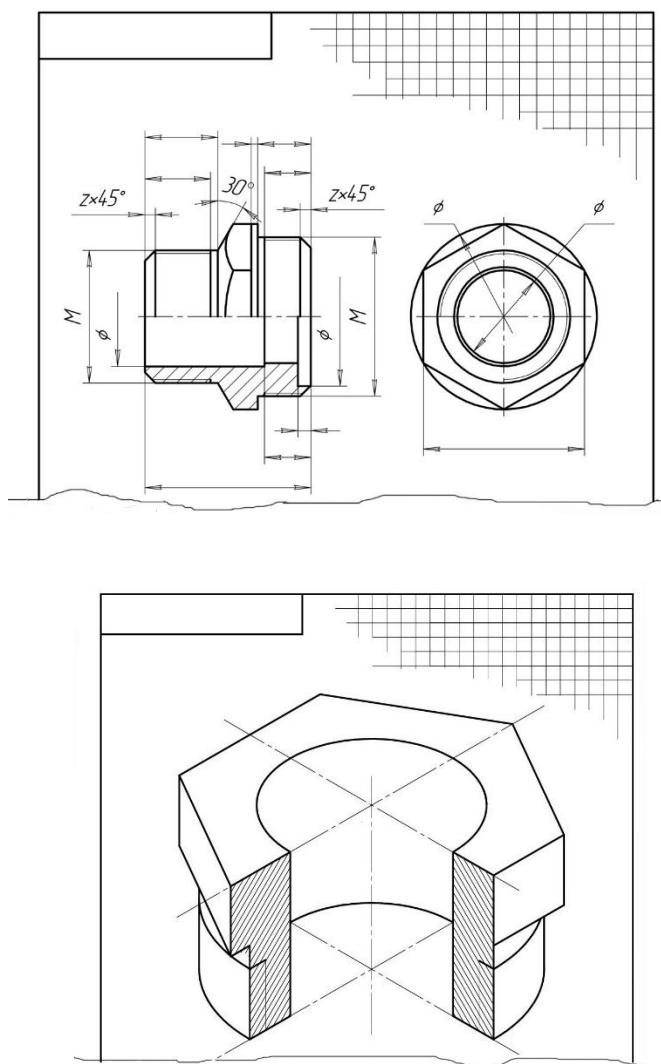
Эскиз штуцера и технический рисунок втулки резьбовой крана проходного сальникового с муфтой и цапкой
